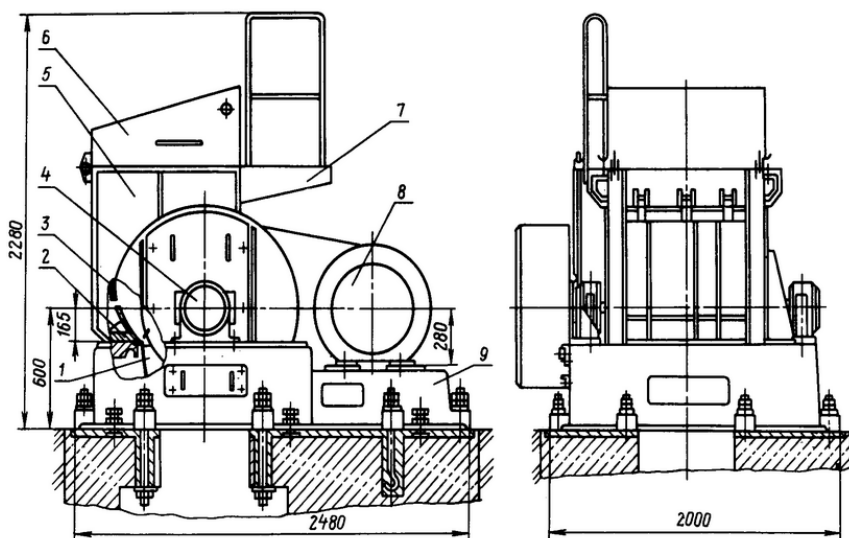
Рубительная машина МРБР8-15Н: 1 - лоток; 2 - контрнож; 3 - крышка контрножа; 4 - ротор; 5 - кожух; 6 - экран; 7 - загрузочный лоток; 8 - двигатель; 9 – станина
